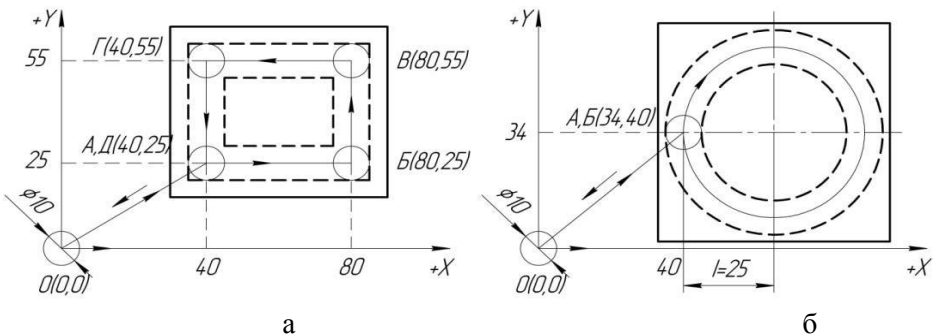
Фрезерування канавки по прямій (а) і по колу (б)
